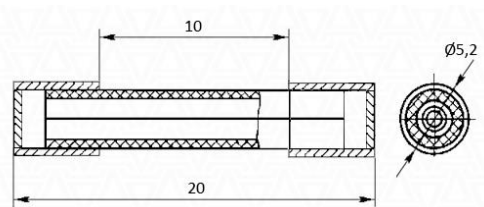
Розміри габаритні ZH214-015 запобіжника
